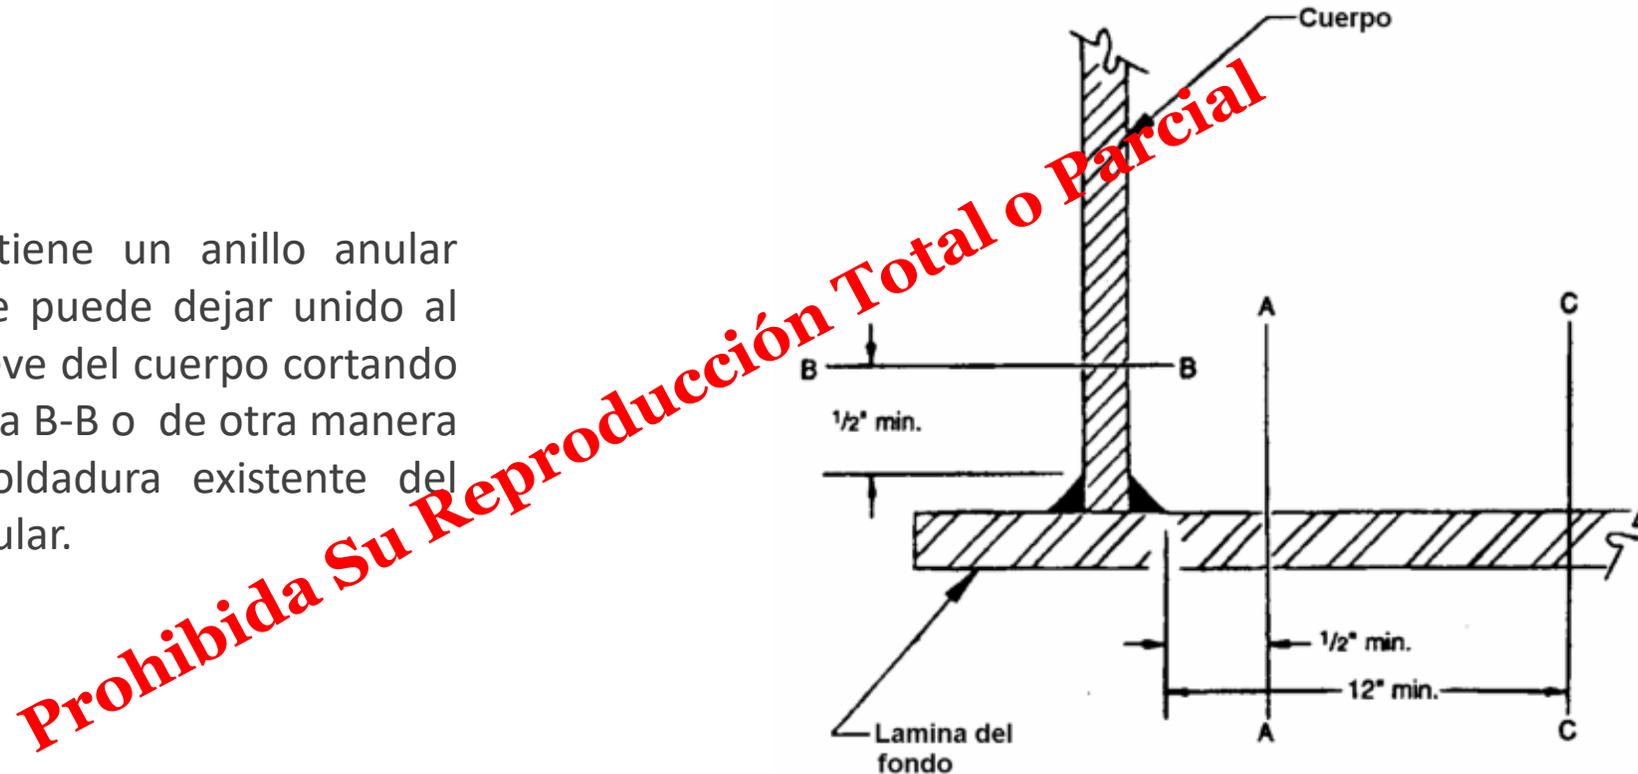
Cuerpo del Tanque y Localizaciones del corte del Fondo
